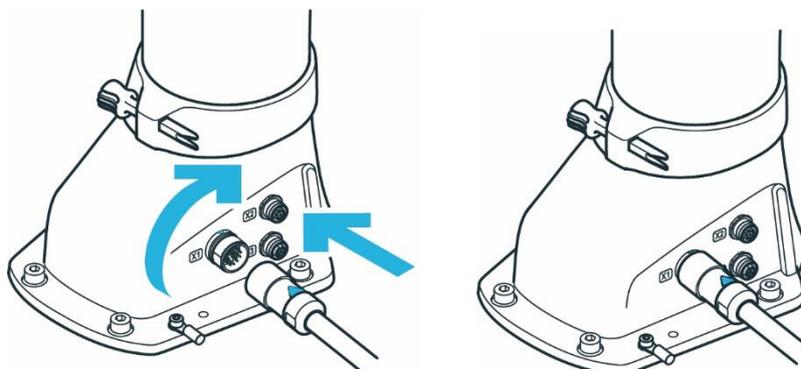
Collegamento del cavo di collegamento al braccio
